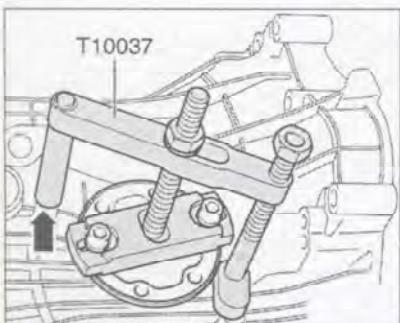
Закрепите на корпусе коробки передач съемник T10037 (стрелка) и снимите правый приводной вал.
